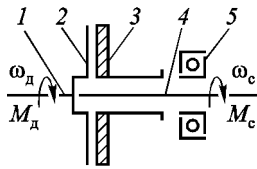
Принципова схема механічного фрикційного зчеплення:
